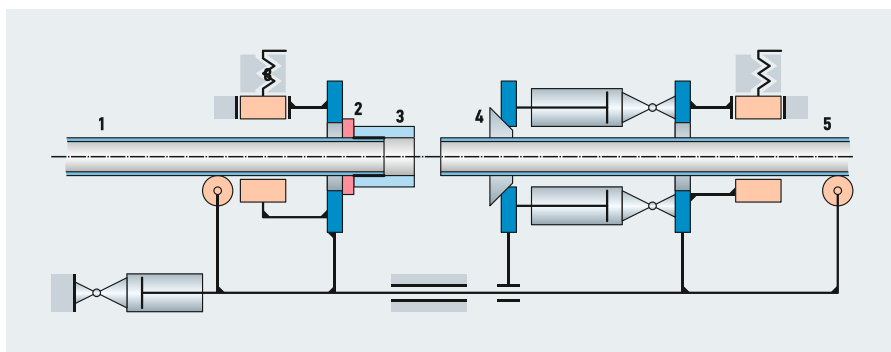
Размещение второй трубы в установке (1 — труба 2; 2 — упор; 3 — муфта; 4 — цанговый зажим; 5 — труба 1)
